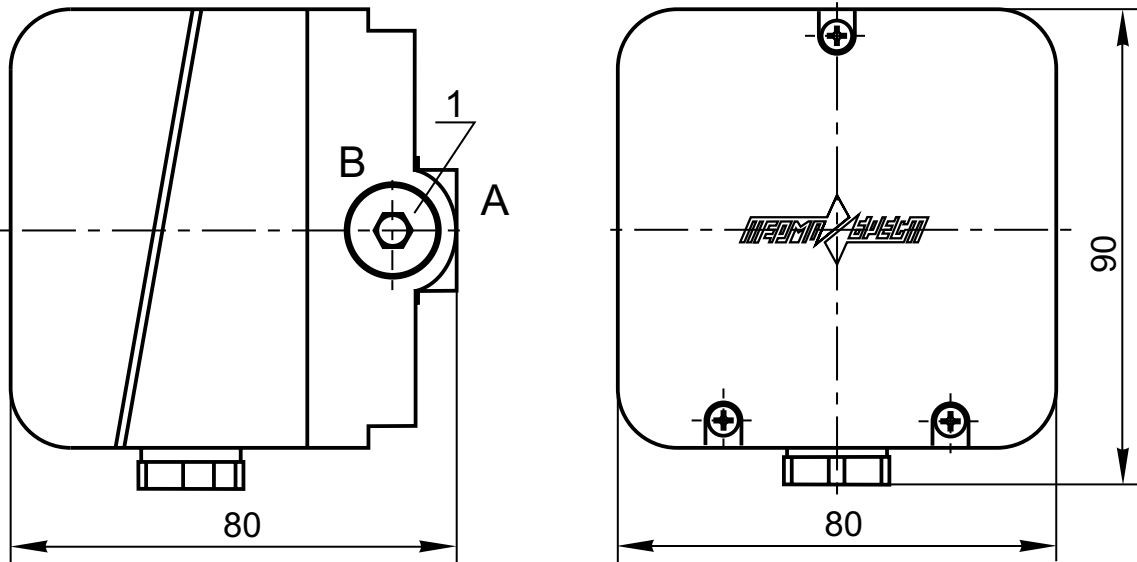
Габаритные размеры датчиков-реле избыточного давления (напора) серии ДРД-Н
